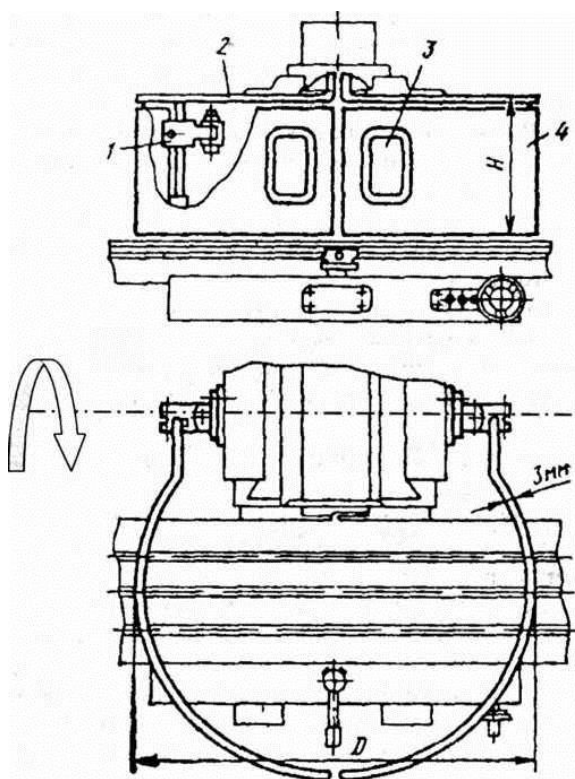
Поворотное ограждение вертикально-фрезерного станка.
